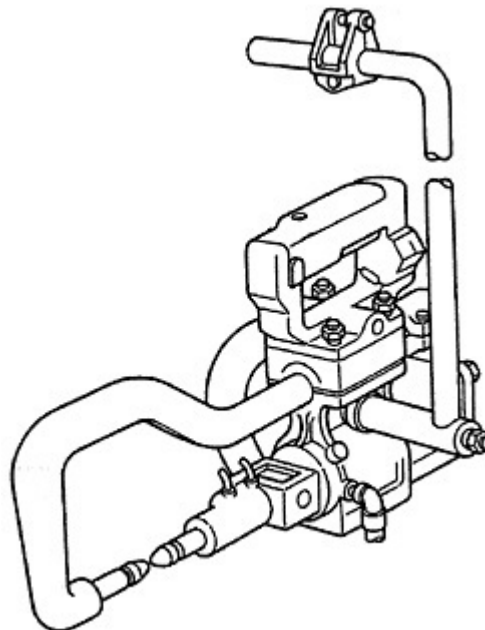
Esquema de uma máquina de solda típica: Tipo C - Cable Gun.
